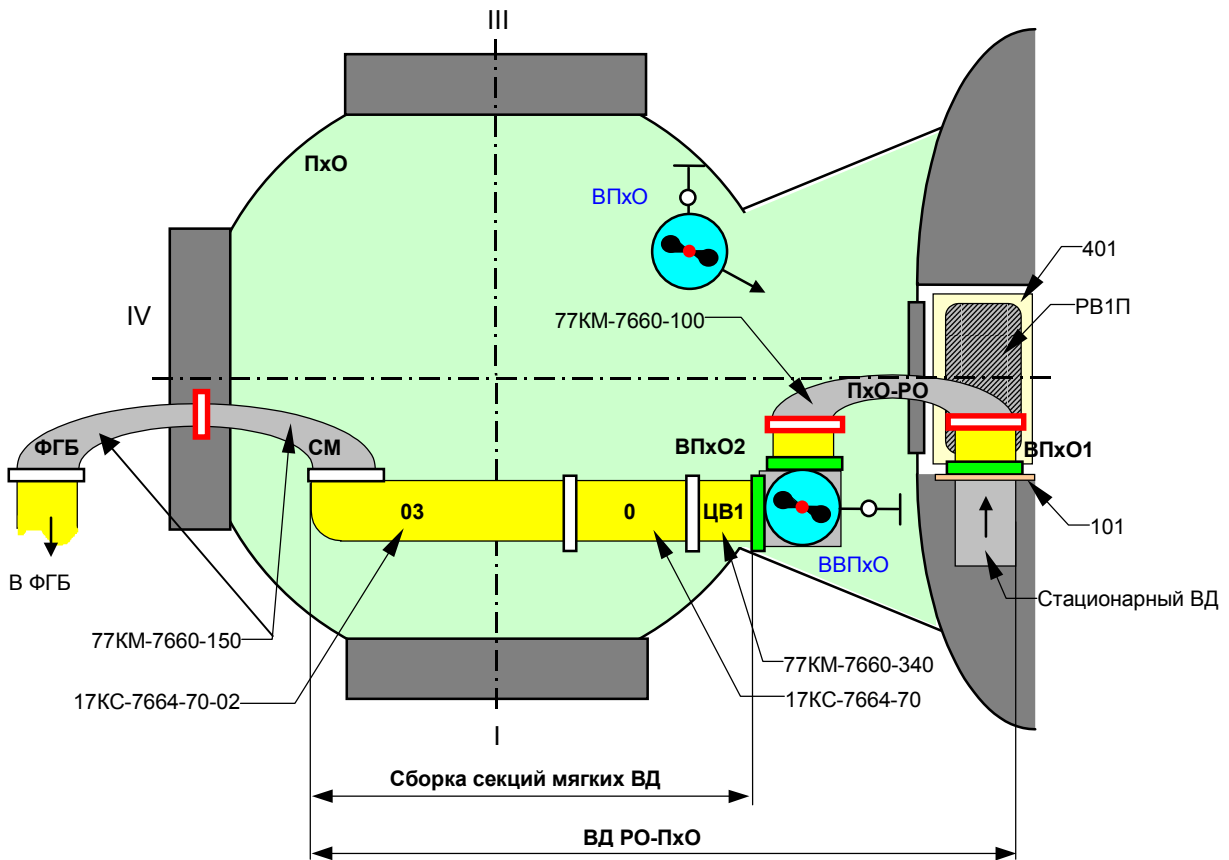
Схема монтажа ВД в зоне РО-ПхО
